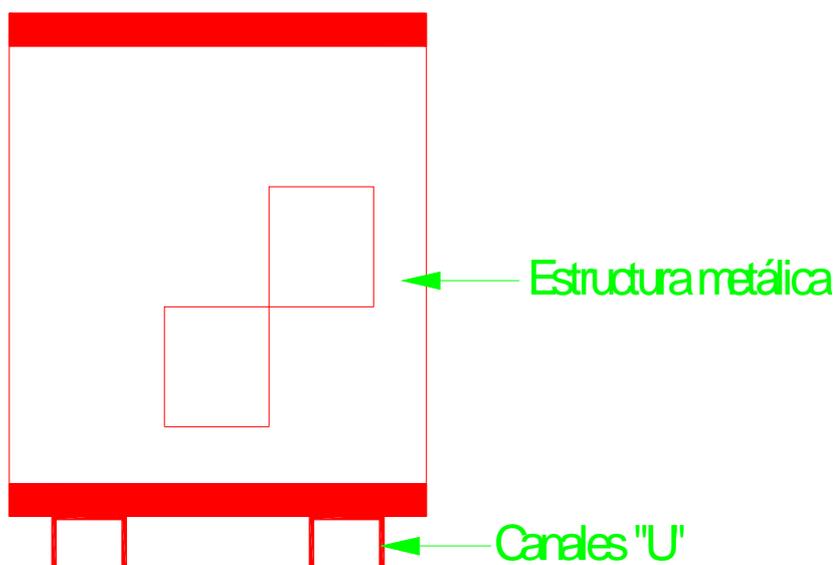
Canales “U” soldados a estructura de horno.
